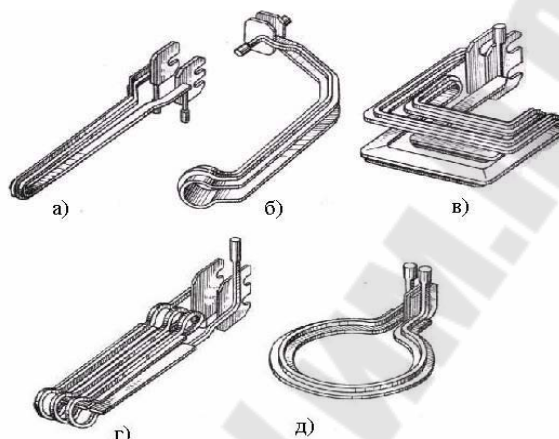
Индукторы для наплавки различных деталей машин: а – петлевой для наплавки лап культиваторов; б – для наплавки плужных лемехов; в – проходной для наплавки долотообразных лемехов; г – трехвитковый для наплавки крыльчаток пескометов; д – для одновременной центробежной наплавки режущих кромок сферических дисков-луцильников
